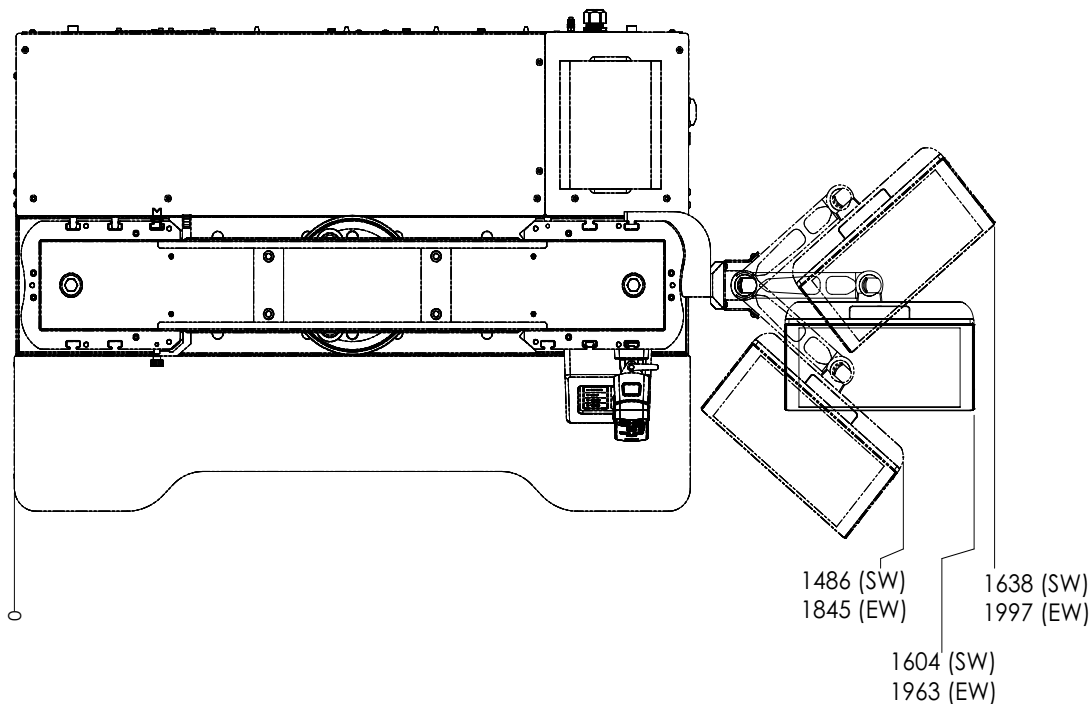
68FM-300 dimensions du bâti – y compris le tableau de bord
